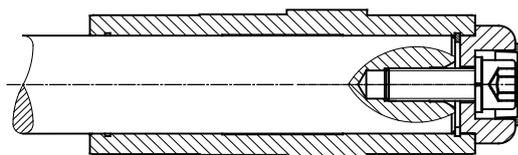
riduttore fissato ad un albero senza spallamento mediante elemento di fissaggio
